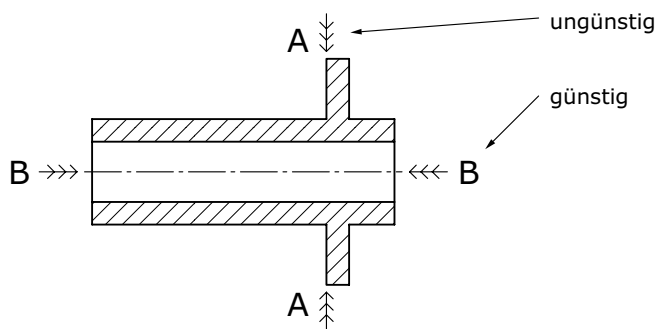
rfZ) Modell- und formtechnisch richtige Gestaltung des Werkstückes
